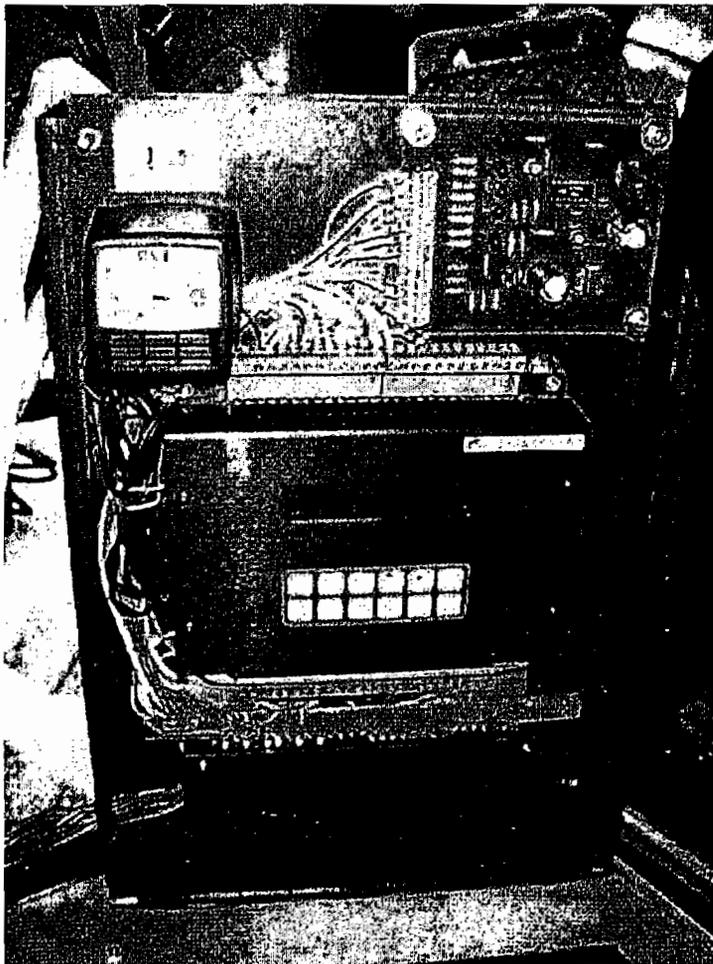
MODULO DE CONTROL SOLDADORA DE PUNTOS
